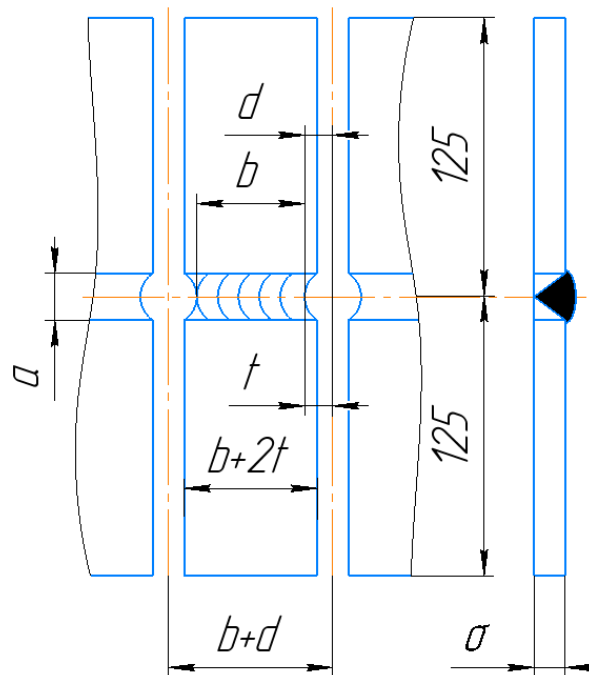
Загальний вигляд плоского зразка з надрізом
